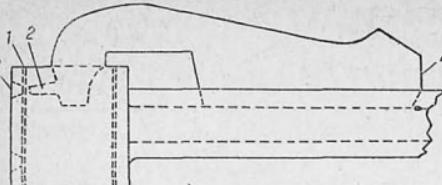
Инструмент для просечки смазочных отверстий верхней головки шатуна
